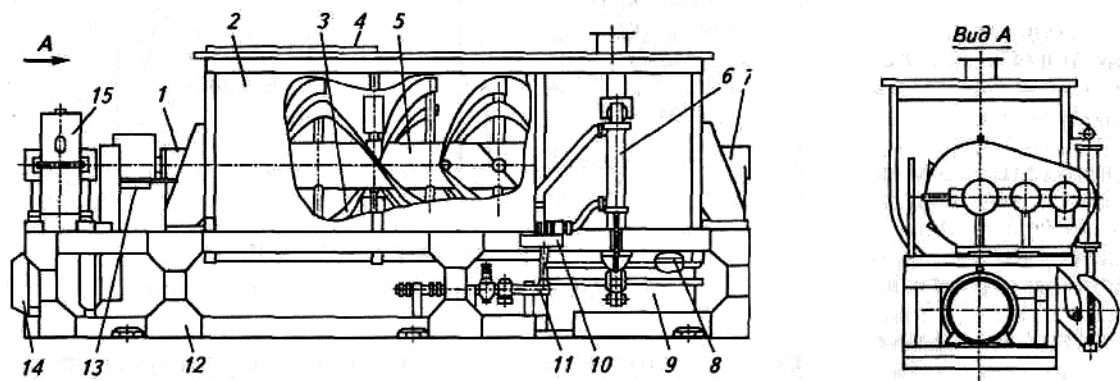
Смеситель СГК-1М: 1, 7—выносные опоры; 2— корпус; 3— спиральная лопасть; 4— фланец; 5— вал; 6— пнев-моцилиндр; 8— выпускной лоток; 9— разгрузочный бункер; 10— пневмораспределитель; 11— тройник; 12— станина; 13— муфта; 14— электродвигатель; 15— редуктор
